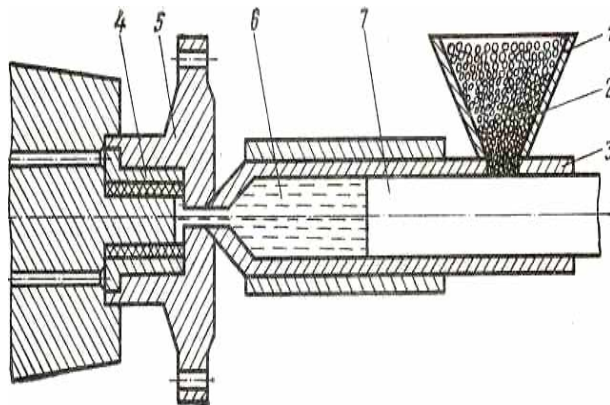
Схема відновлення деталей литтям під тиском: 1 – бункер; 2 – полімерний матеріал; 3 – циліндр; 4 – деталь; 5 – пресформа; 6 – розплавлений полімерний матеріал; 7 – поршень
